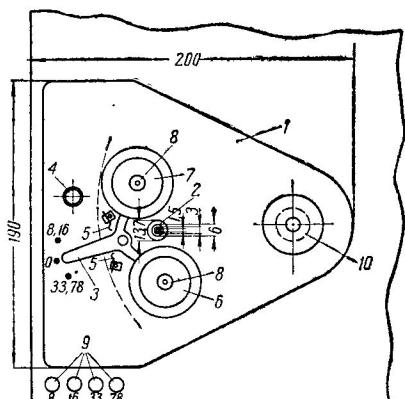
Панель проигрывателя: 1 — металлическая панель проигрывателя; 2 — четырехступенчатая насадка; 3 — рычаг переключения скоростей; 4 — поворотная кнопка; 5 — контакты; 6 — передний обрезиненный ролик; 7 — задний обрезиненный ролик; 8 — шариковые подшипники; 9 — линзы сигнальных лампочек; 10 — втулка оси диска.
